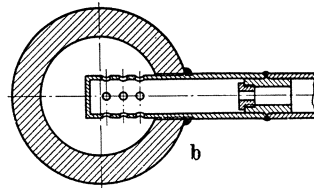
Schnitt durch ein Sammelrohr mit eingeschweißtem Heizrohr und Düse eines La Mont-Kessels (Hochdruckausführung).
